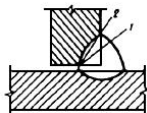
Схема расчетных сечений сварного соединения с угловым швом
